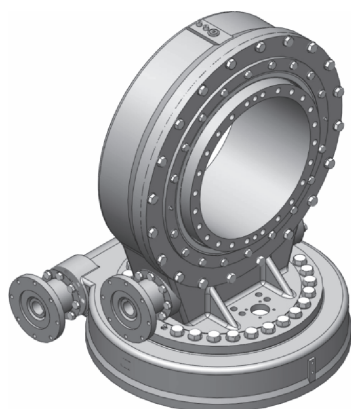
Внешний вид опорно-поворотного устройства DAD6-Z0-LM
